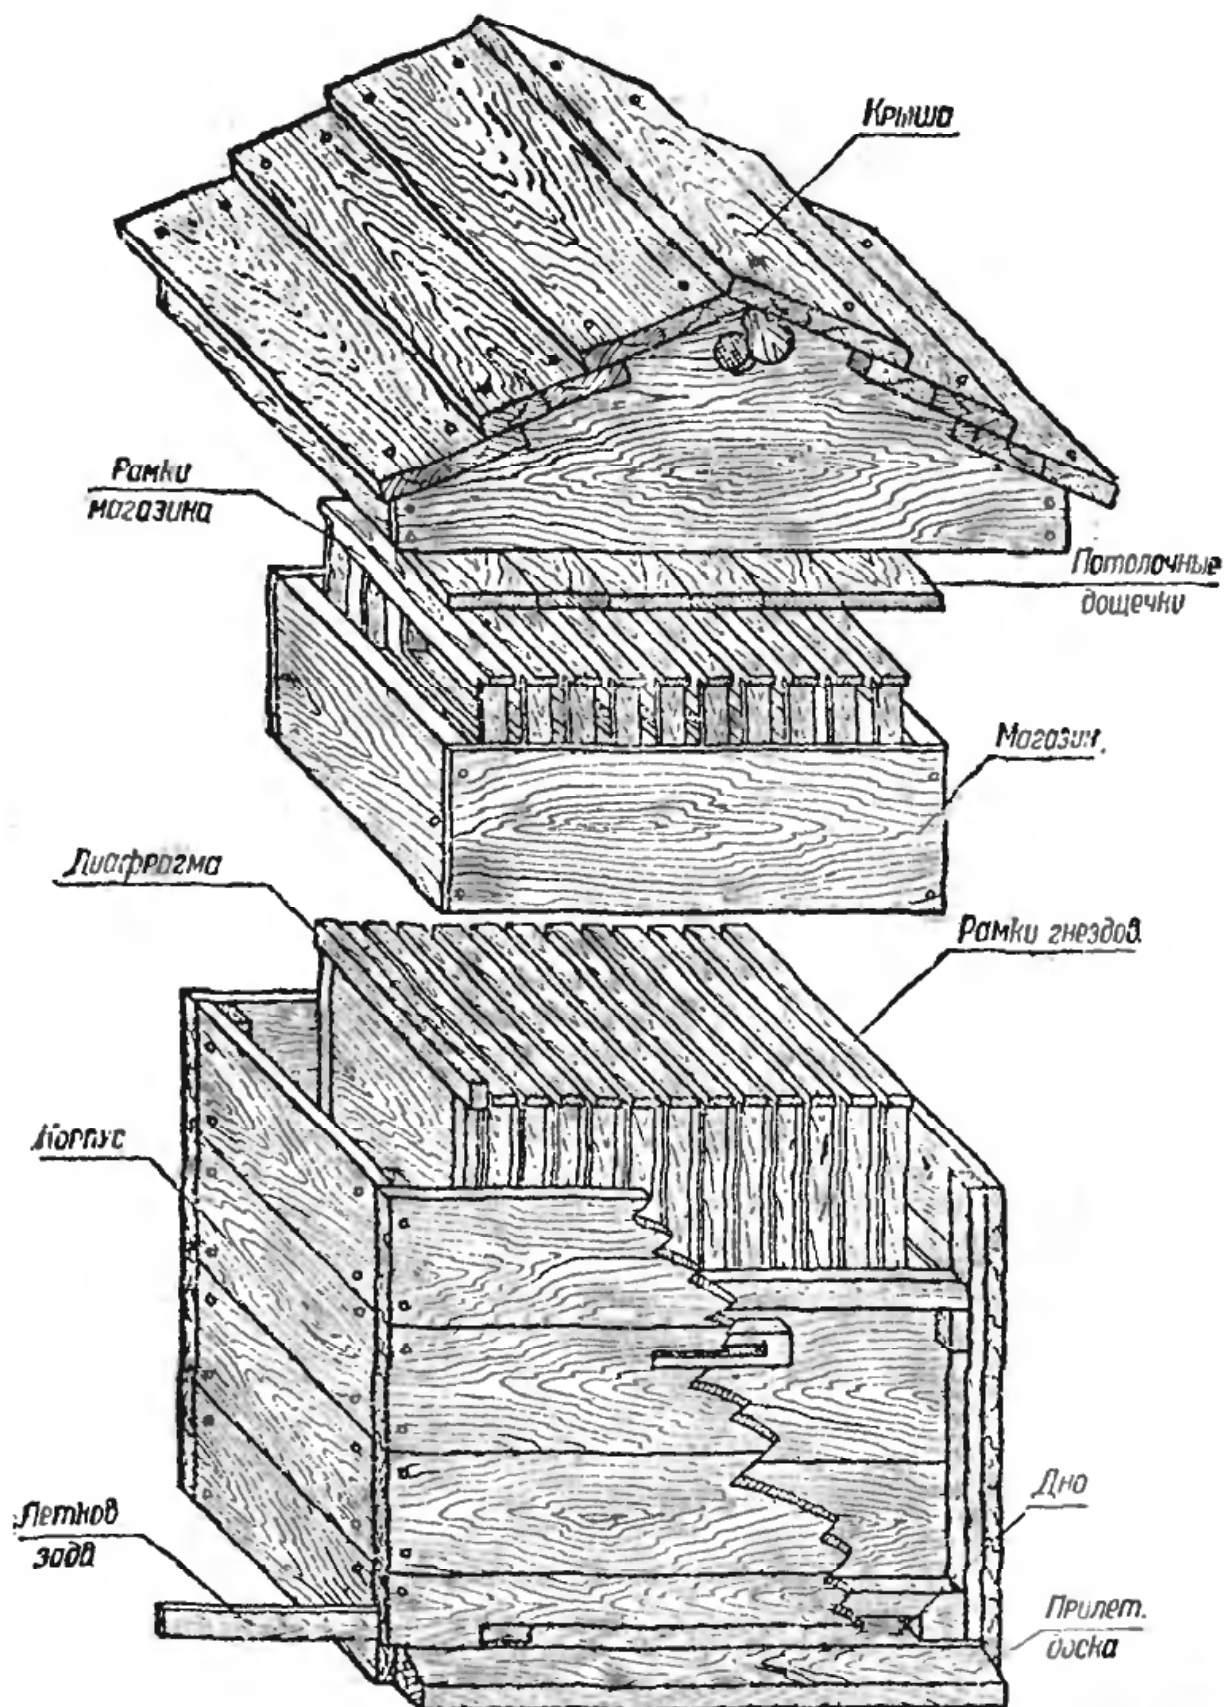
Двустенный 12-рамочный улей Далана-Блатта; общий вид двустенного улья.
